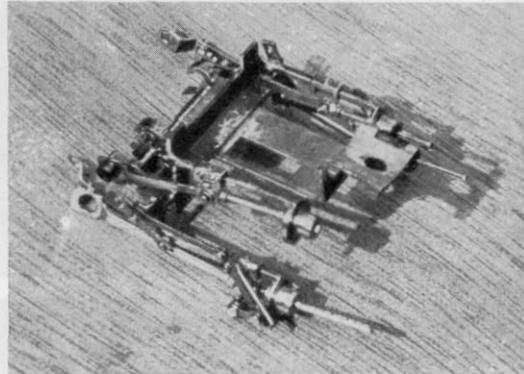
Steuerungsträger und Steuerung; wie dieses Teil auf das Fahrgestell aufgesetzt wird, zeigt Abb. 23.
